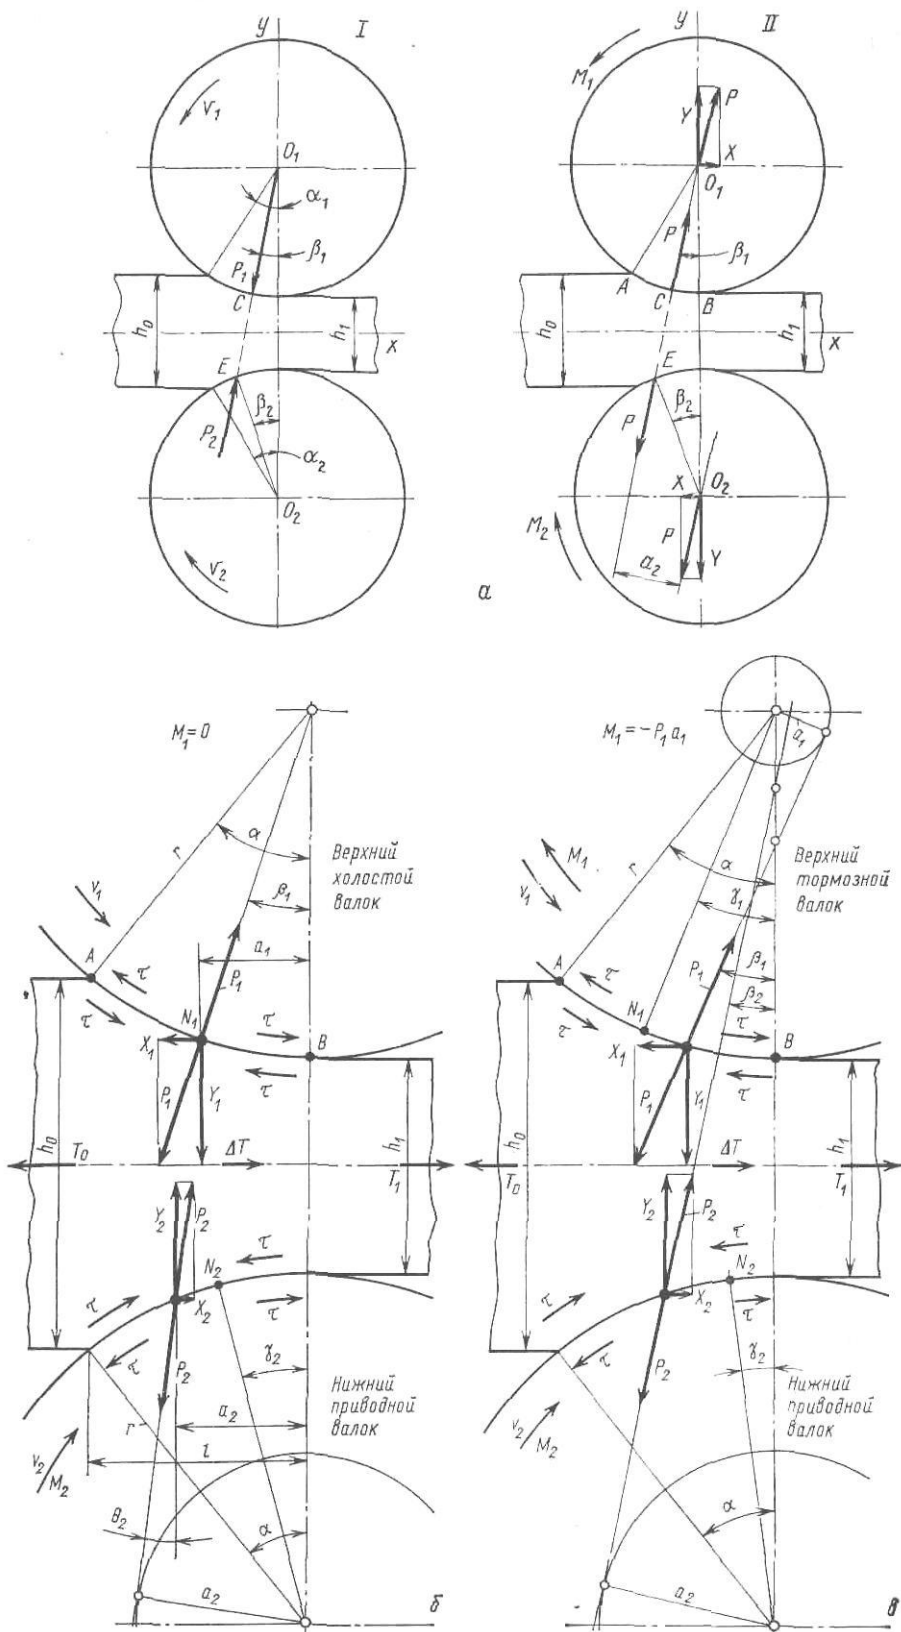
Направление усилий при прокатке на стане с холостым (верхним) валком: а — без натяжения; б — с натяжением полосы; в — с натяжением и с учетом трения в подшипниках не приводного валка; I — силы, действующие от валков на металл; II — то же, от металла на валки
